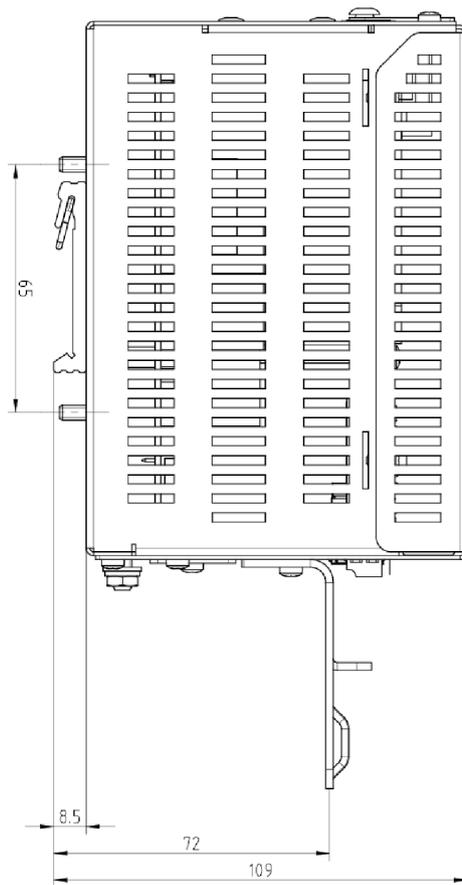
Esquema acotado de IE Switch X302-7EEC - Vista lateral
